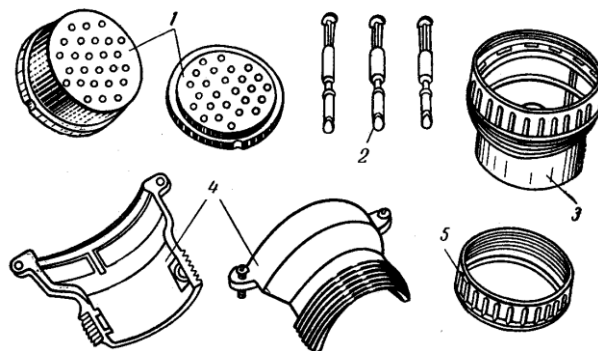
Основные детали и узлы цилиндрических приборных разъемов. 1 - изоляторы, 2 – контакты, 3 – корпус, 4 – патруб-бок, 5 –кабельный зажим.
